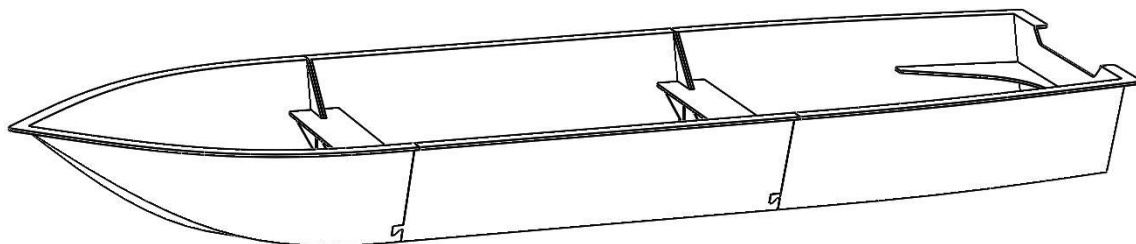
Jolle-versjon sett fra oversiden.
